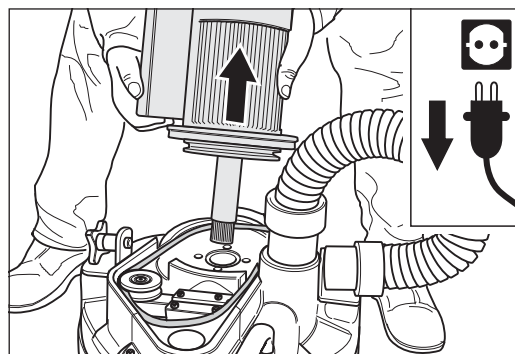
Den Motor nach oben vom Maschinengehäuse abnehmen und den Keilriemen entfernen.
